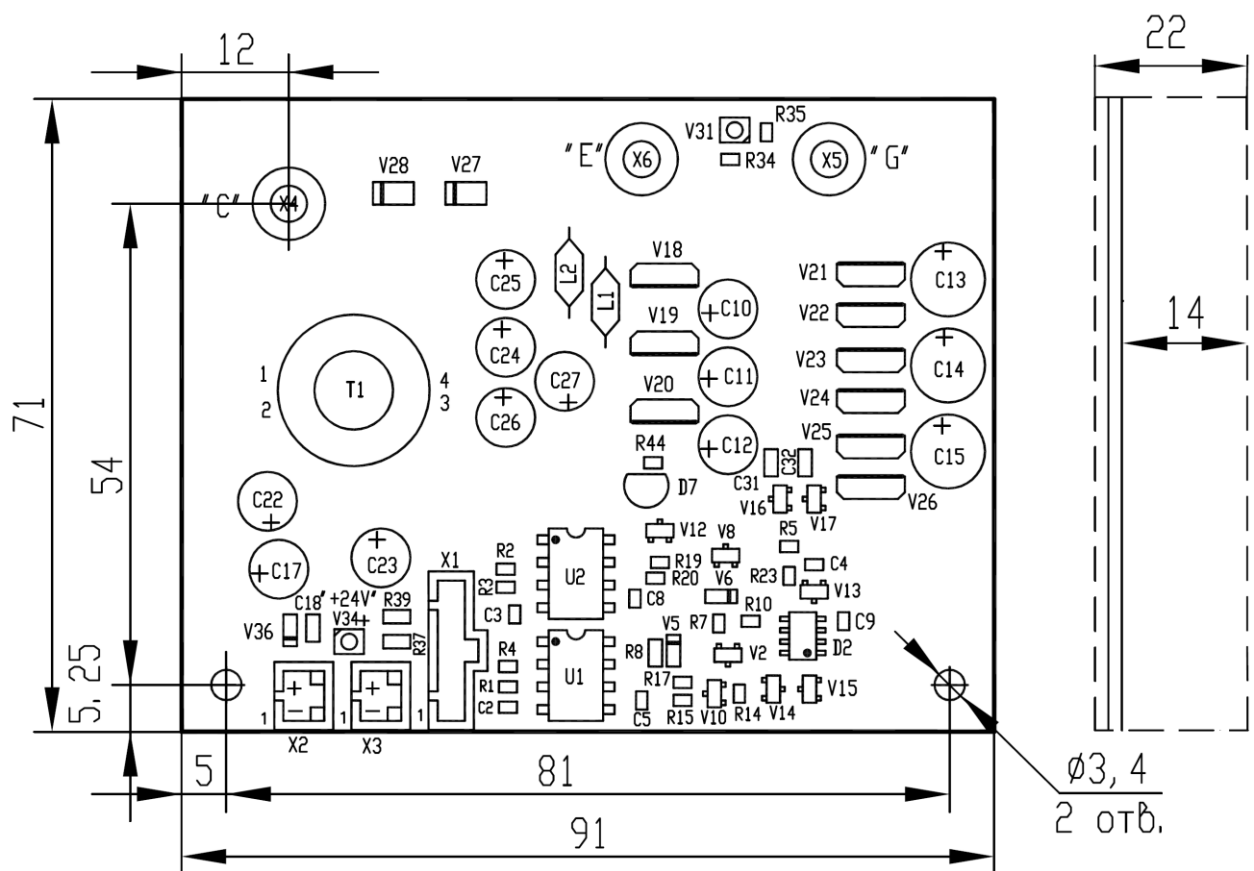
Габаритные и конструктивные размеры платы драйвера ДРИ11-30-17-20П1Н-1
